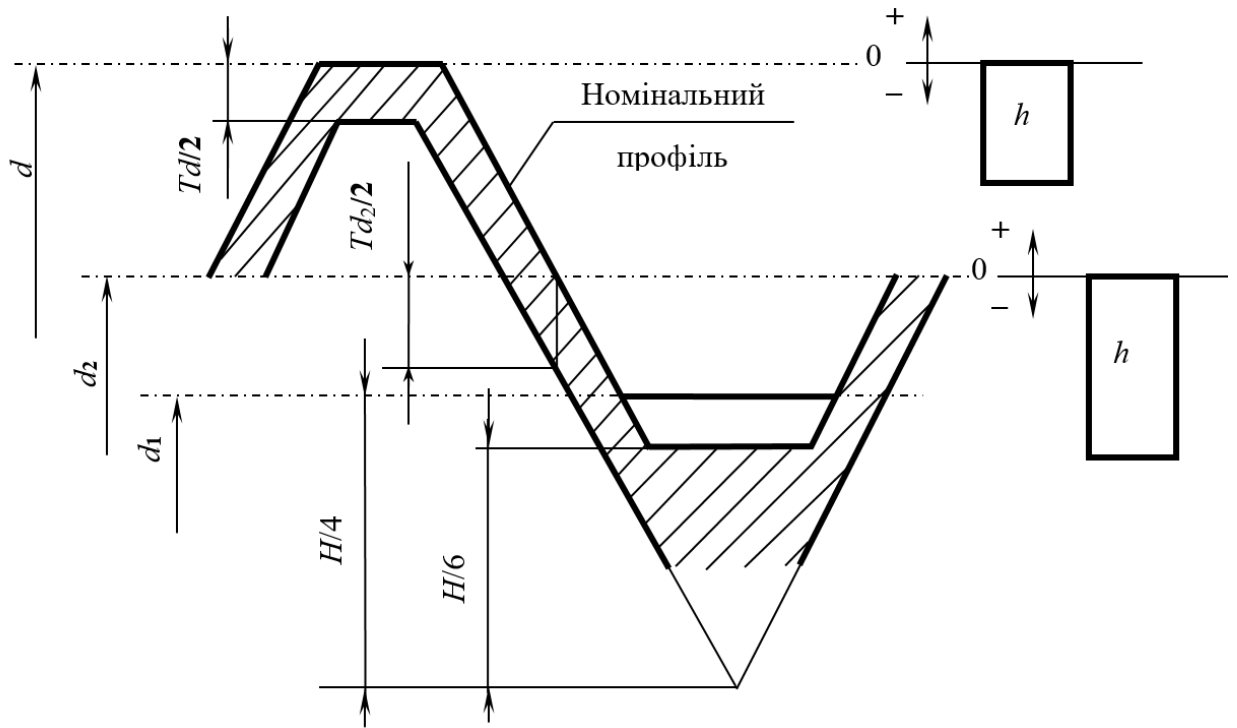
Схема розташування полів допусків болта.
